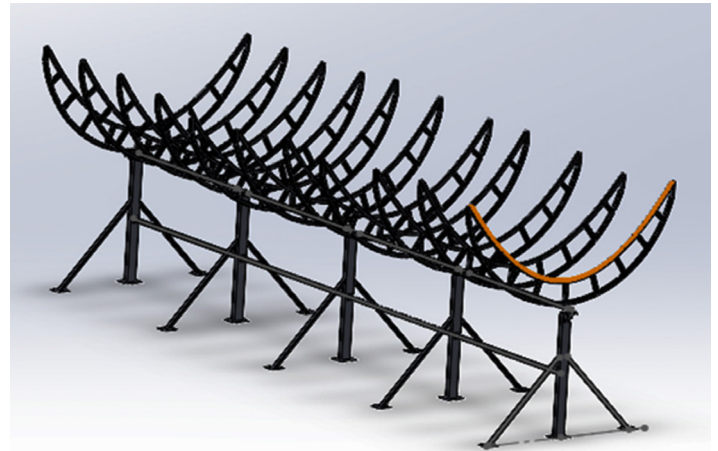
Base final con las 11 estructuras acopladas al eje de torsión. Fuente: elaboración propia
